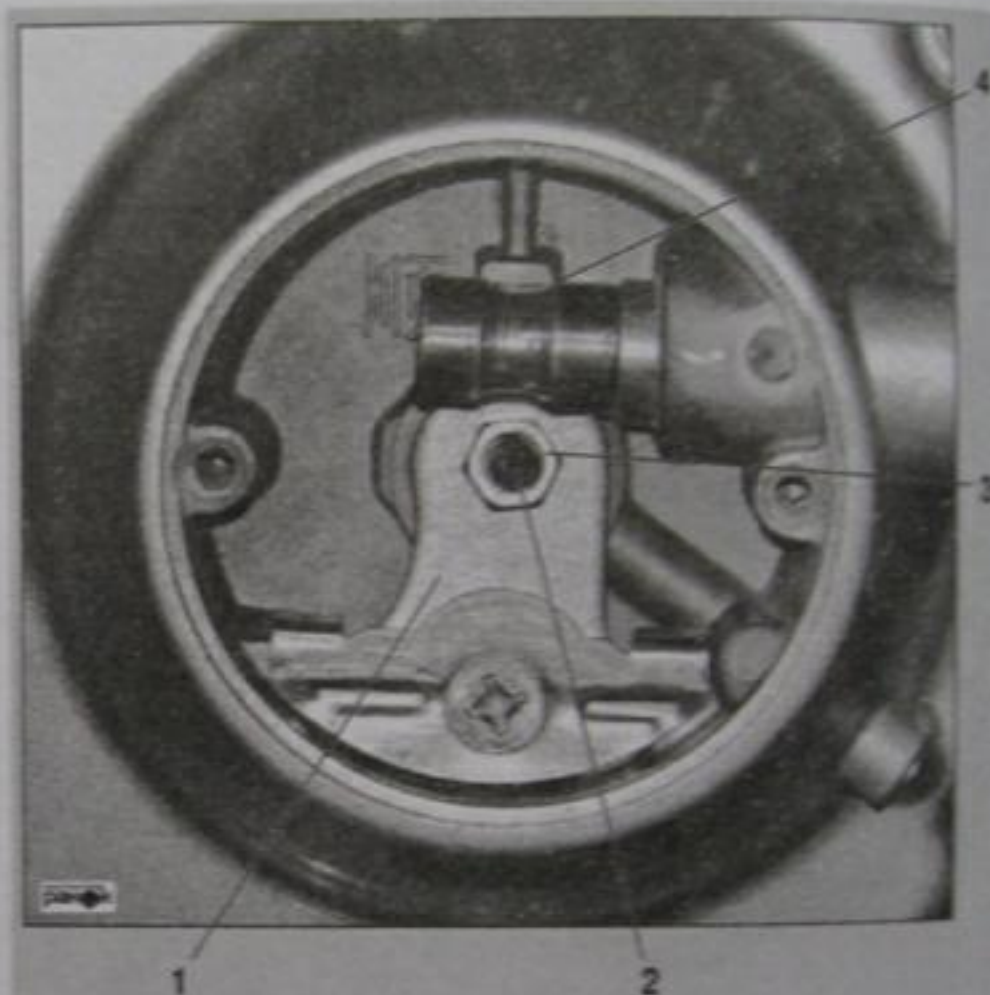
Расположение элементов привода и регулировки механизма выключения сцепления: 1 – рычаг привода механизма выключения сцепления; 2 – стопорная гайка («контргайка»); 3 – регулировочный винт механизма выключения сцепления; 4 – вал выжима сцепления
